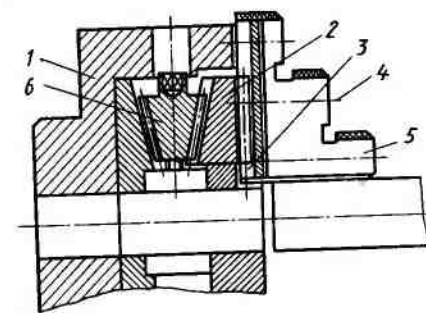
Схема работы самоцентрирующегося трехкулачкового патрона: 1 — корпус, 2 — спиральный диск, 3 — рейка, 4 — винты, 5 — накладные кулачки, 6 — коническое зубчатое колесо
